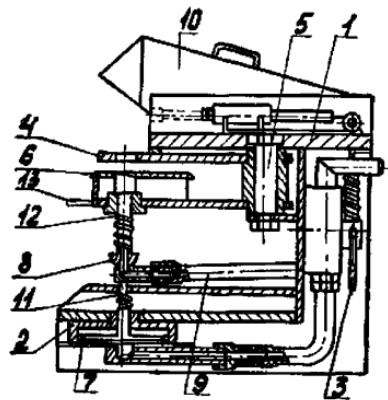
Пресс пневматический для вырубки отверстий в прокладках:
